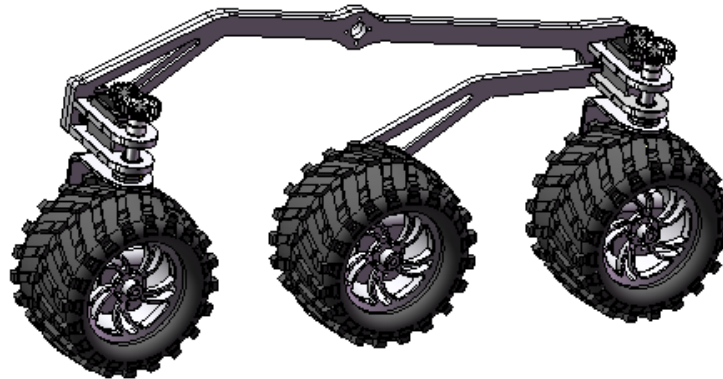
Diseño del ensamble del subconjunto lado derecho.
